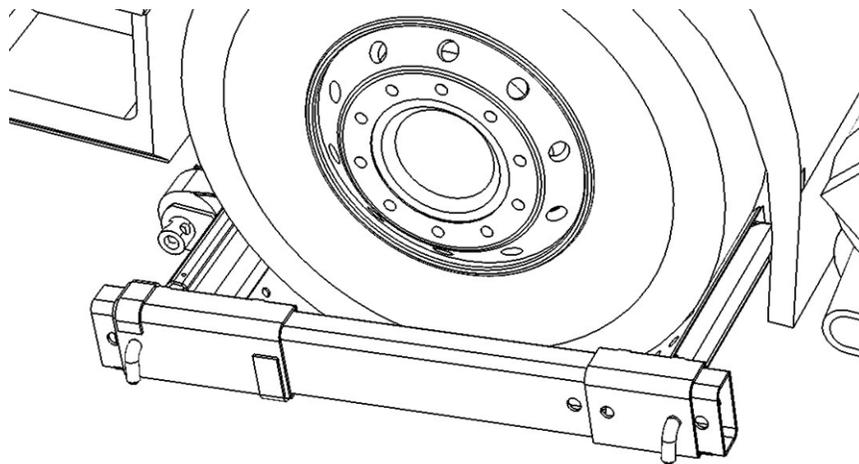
ARRIÈRE D'UN LÈVE-PNEUS
